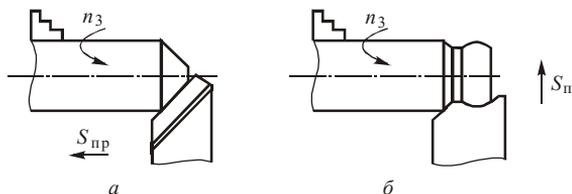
Получение конической (*a*) и фасонной (*б*) поверхностей на токарном станке
